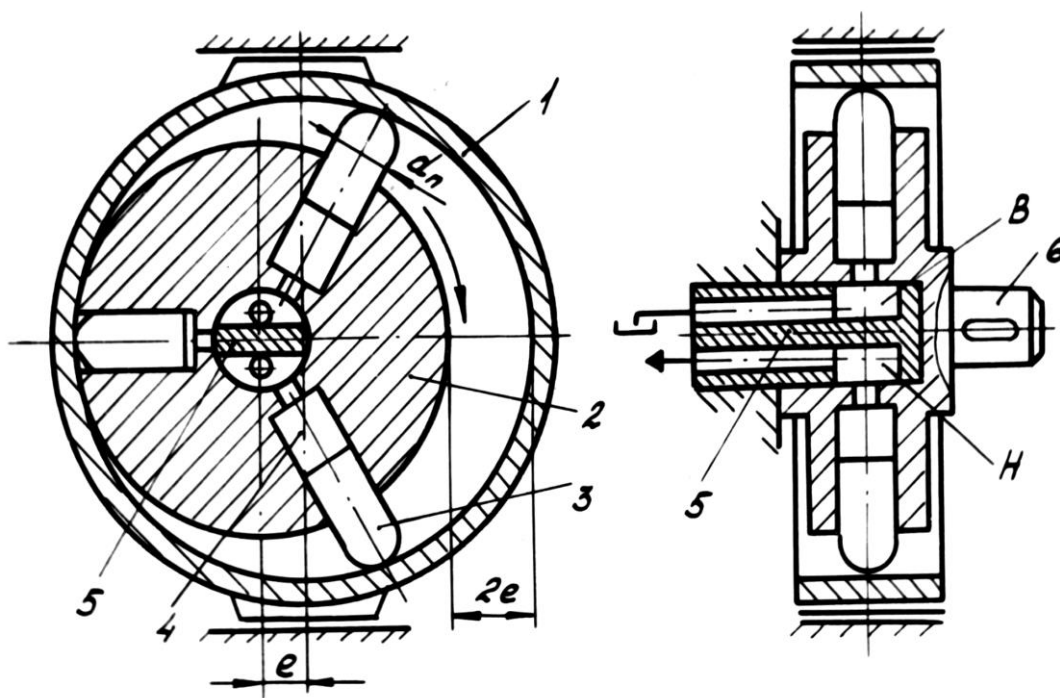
Схема радиально-поршневого насоса однократного действия: 1 – статор (корпус); 2 – блок цилиндров (ротор); 3 – поршень (вытеснитель); 4 – рабочая камера; 5 – цапфенный распределитель; 6 – приводной вал
